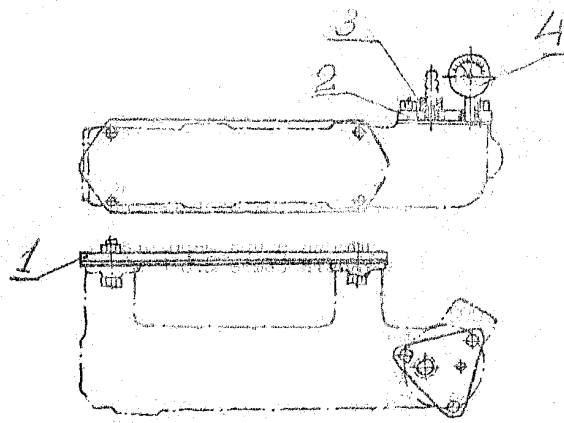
Приспособление для гидравлических испытаний трубопроводов:
